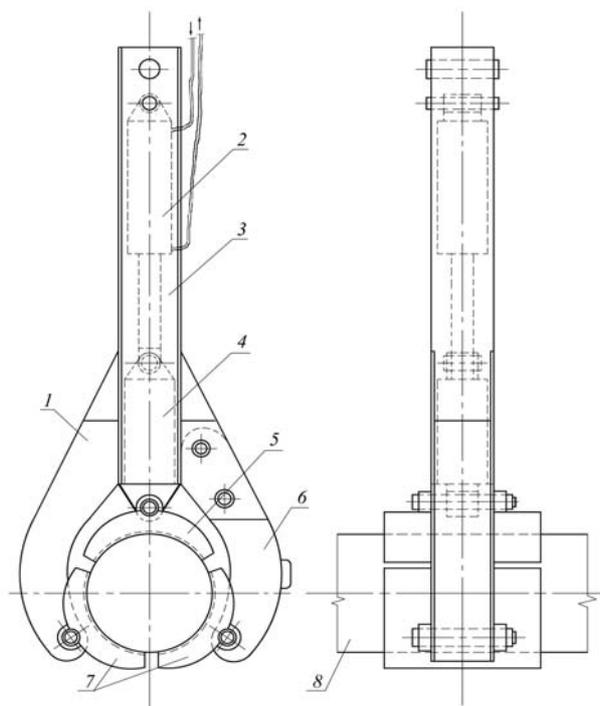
Схема гидравлического захватного устройства: 1-корпус; 2-гидроцилиндр; 3-стойка корпуса; 4-шток направляющий; 5,7-фрикционные накладки съемные; 6-затвор замыкающий; 8-трубопровод
